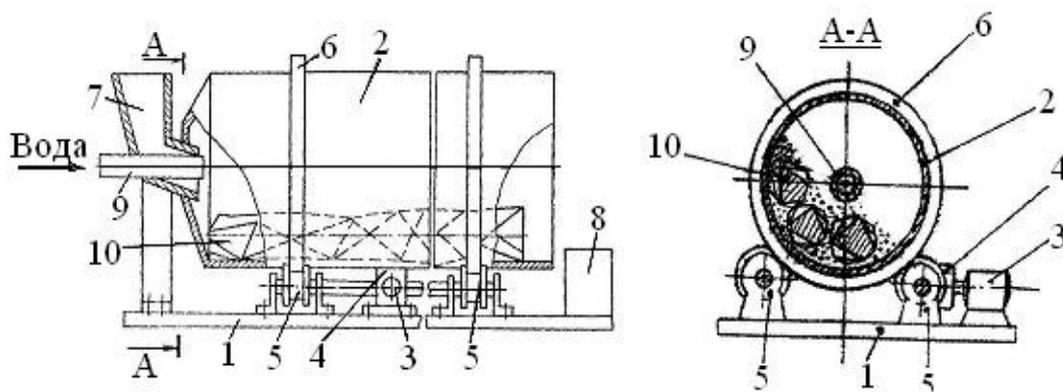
Стержневой бетоносмеситель (варианты) (1 – станина; 2 – барабан; 3 – электродвигатель; 4 – редуктор; 5 – четыре роликовых опоры; 6 – два обода; 7 – устройство для загрузки; 8 – устройство для разгрузки; 9 – трубопровод; 10 – стержни-катки)
